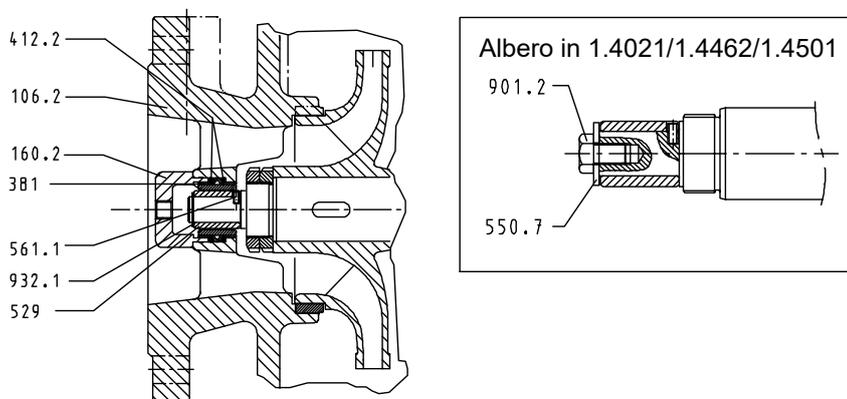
Smontaggio cuscinetto a scorrimento - bocca aspirante assiale
